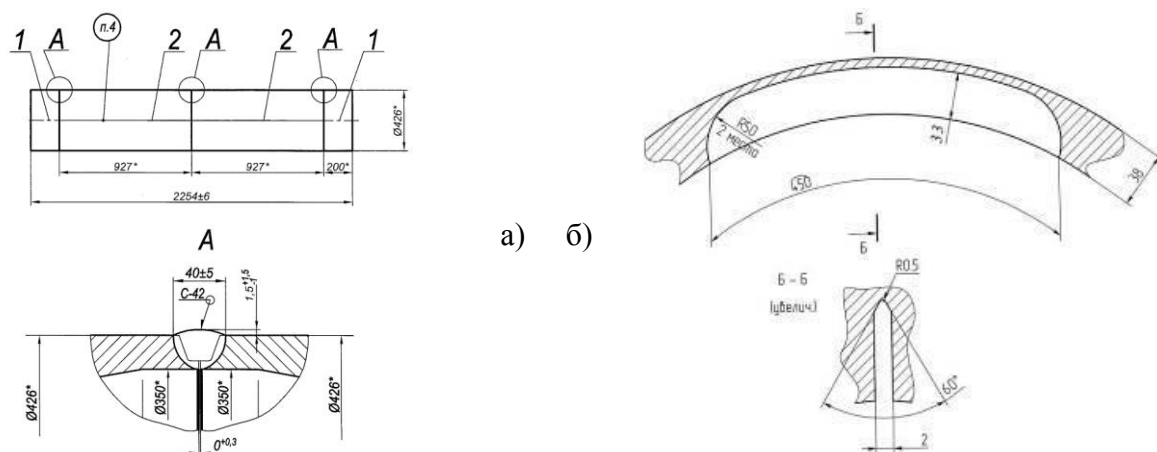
а) Чертеж модели прямолинейного участка трубы со сварными швами;
